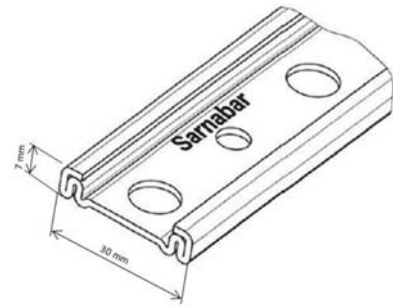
Coupe du rail de fixation Sarnabar® 6/10
